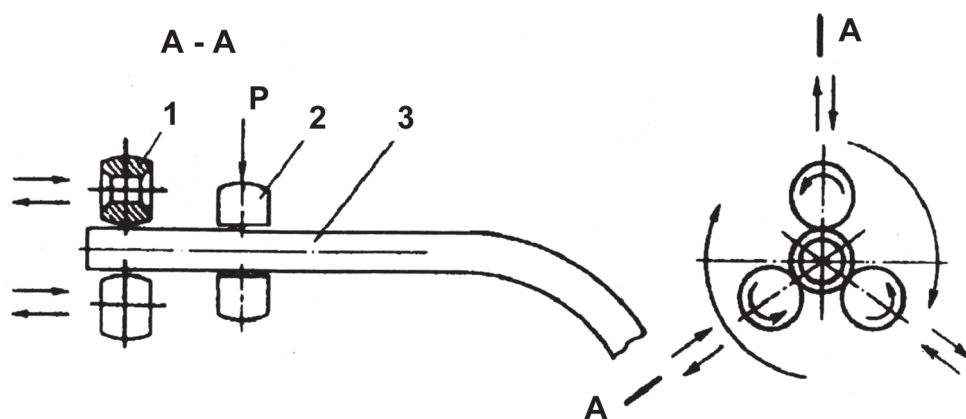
Схема калибровки концов труб обкаткой роликами:
